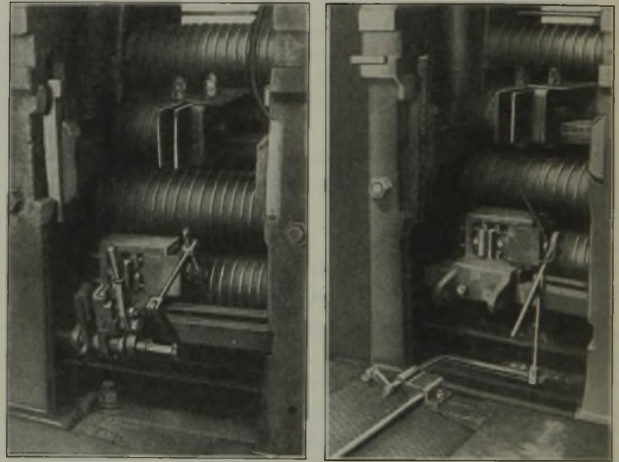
Neue anstellbare Stauchkasten im Walzgerüst eingebaut; links mit vorgeschalteter Einstoßvorrichtung, rechts mit Fußhebelanstellung.
